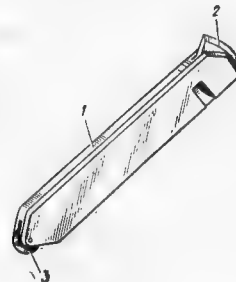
1 — корпус; 2 — нож; 3 — ролик
